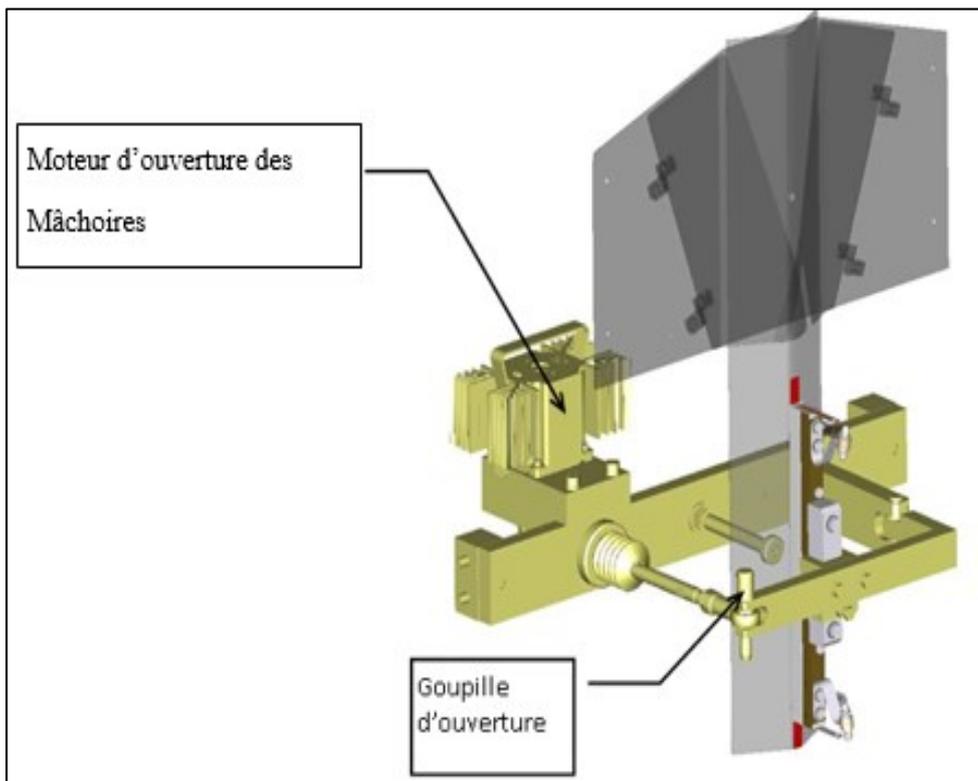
dessin technique pour système de soudure verticale.[16]
